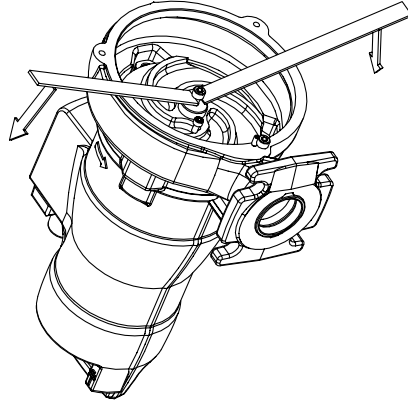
Insertar la unidad del rotor en la tapa de aspiración
